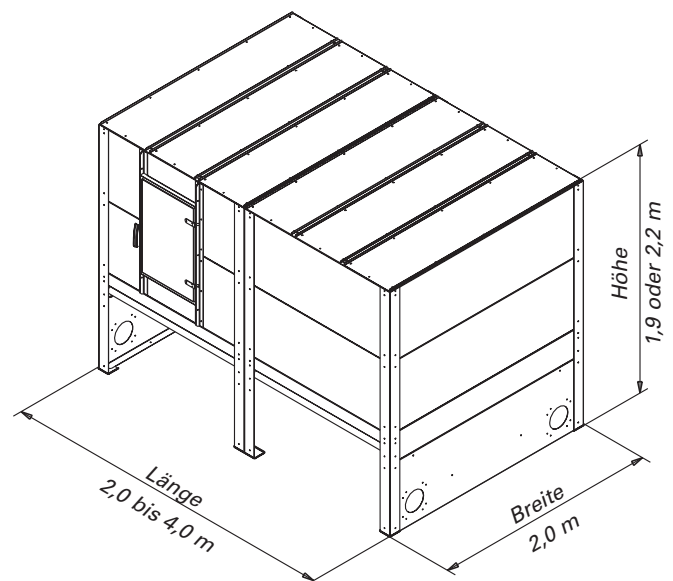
Stahlblech-Tanks mit Breite 2,0 m
